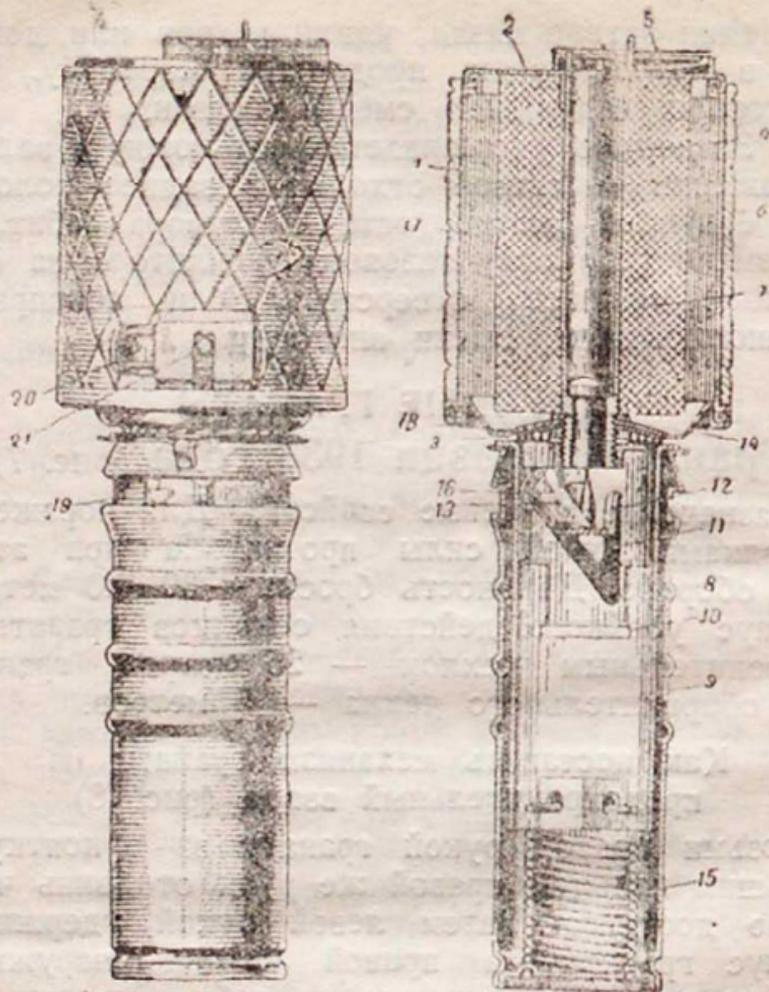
Граната образца 1933 года: 1—корпус; 2—крышка корпуса; 3—тормозящая звезда; 4—центральная трубка; 5—задвижка запала; 6—оборонительный чехол; 7—разрывной заряд; 8—наружная трубка рукоятки; 9—внутренняя трубка рукоятки; 10—вкладыш; 11—прорези; 12—боевая скоба; 13—ударник; 14—дно корпуса; 15—боевая пружина; 16—предохранитель запала; 17—лента; 18—опорные гайки; 19—задвижка предохранителя; 20—задвижка чехла; 21—штифт для закрепления чехла.
